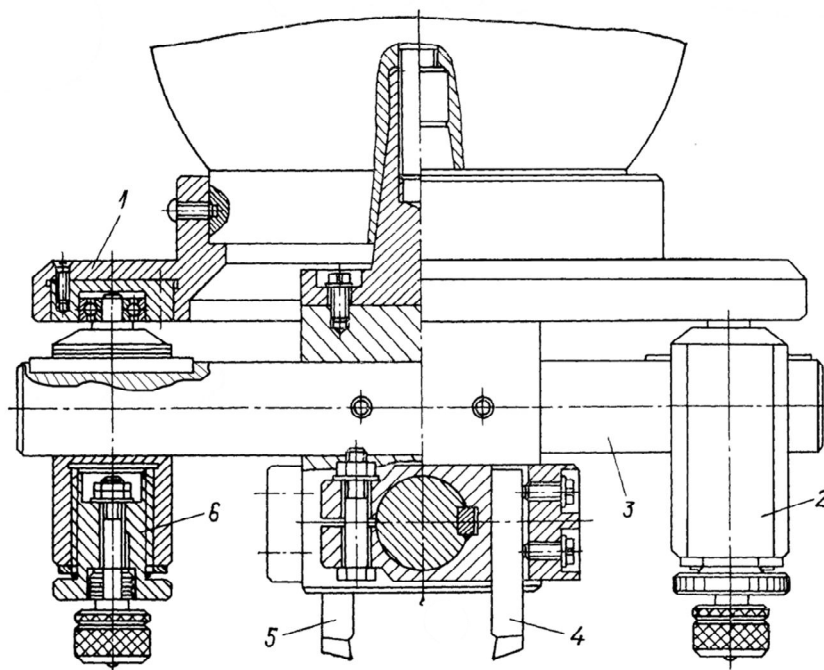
Віброголовка для одночасного торцевого фрезерування і вібронакочування плоскої поверхні
